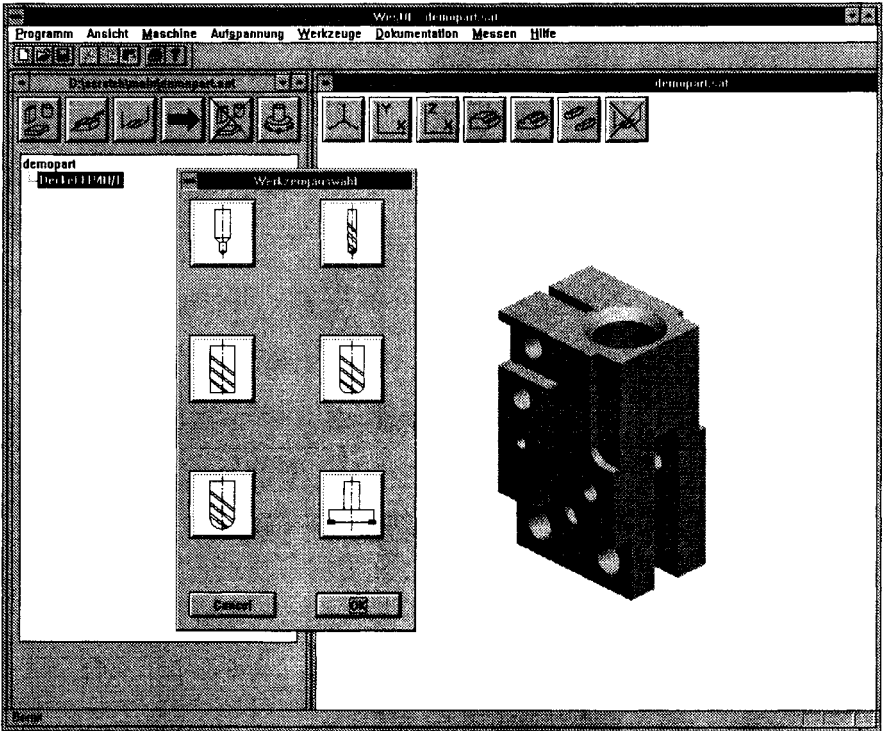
Werkzeugabhängige Bearbeitungsobjektdefinition
